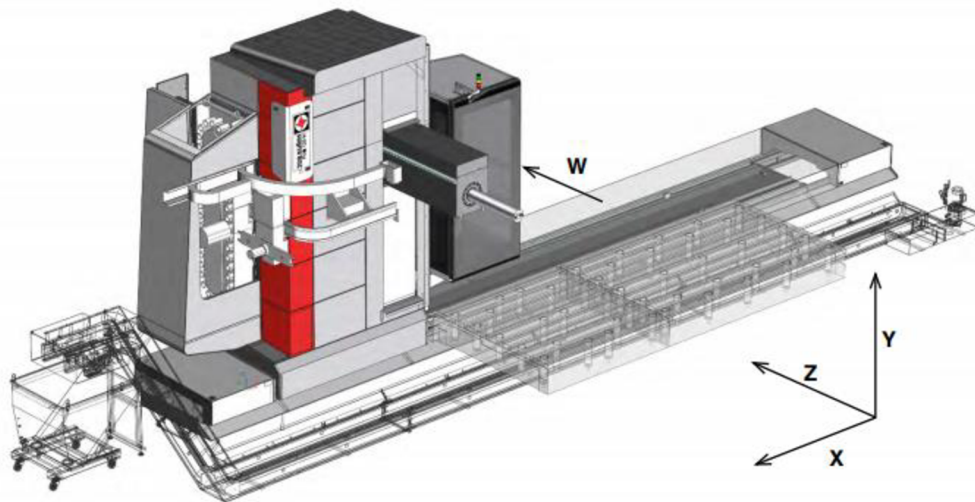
Souřadnicový systém stroje FRF, TOS Kuřim [5]
